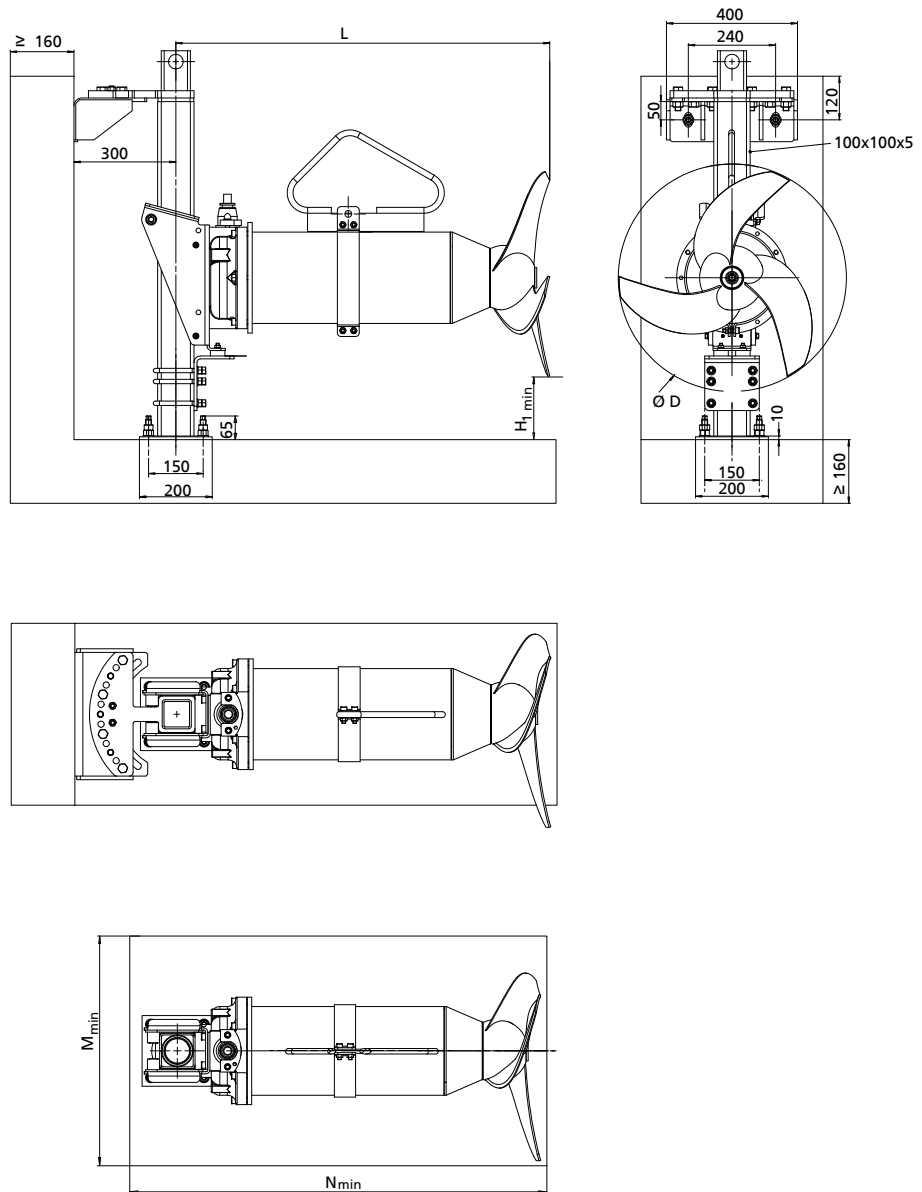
Установка принадлежностей 22 — Атаміх 400 (только типоразмер 4135) / 600
